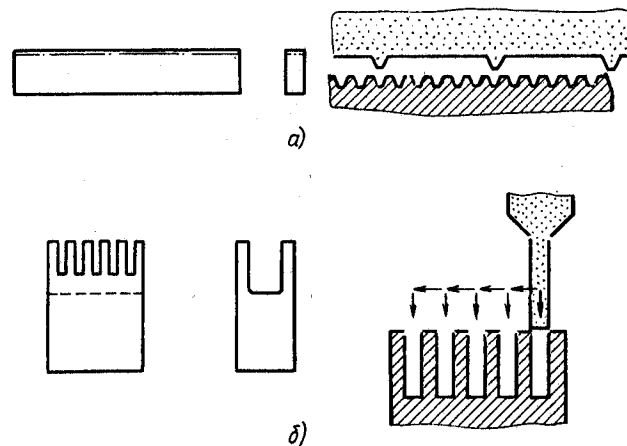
Схема профильного шлифования с шаговой подачей при обработке мелко модульной зубчатой рейки (а) и пресс-формы для изготовления рамок с внешними выводами интегральных микросхем (б)
